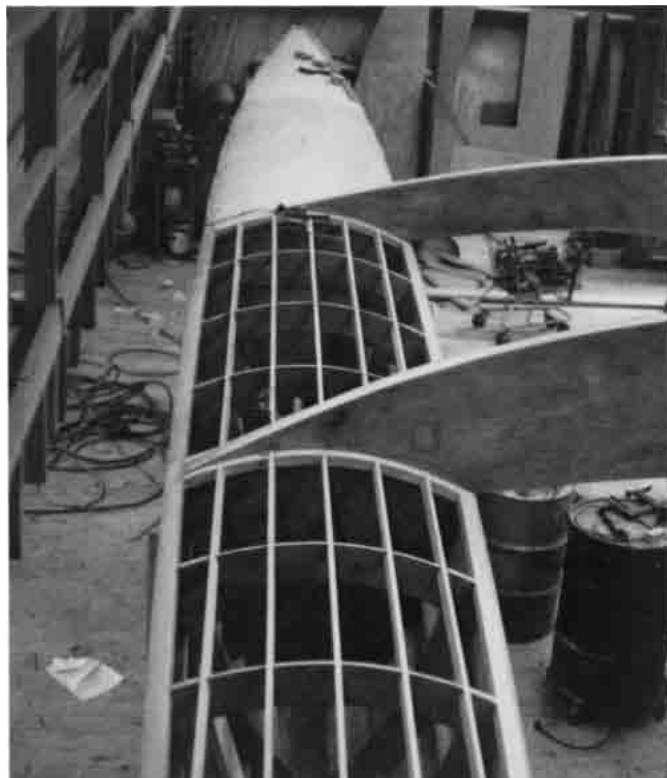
Dieselben Decksbalken mit eingebauten Stringern, fertig zum Auflegen des Decks.
